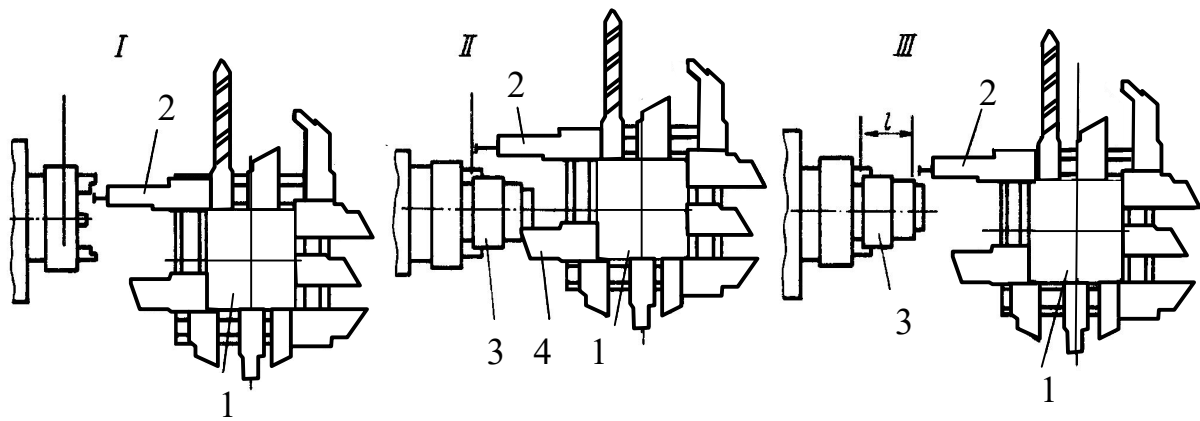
Схема обробки заготовки на верстаті з ЧПК, оснащеного системою автоматичної корекції статичного налагодження
